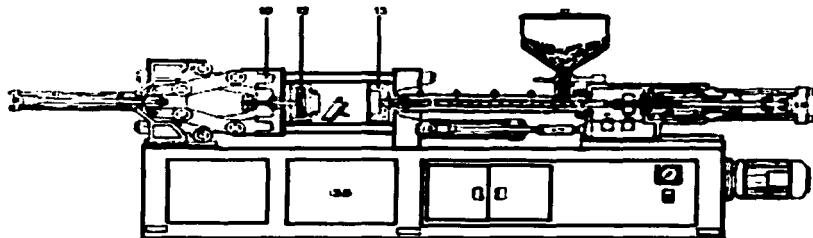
Sección longitudinal de una máquina de moldeo por inyección con husillo recíproco y rodillera doble equipada con motor hidráulico de pistones axiales para accionar la rotación del husillo. La máquina se muestra con el molde abierto en el momento de expulsión de la pieza moldeada 12. Medio molde móvil 13. Medio molde fijo.
